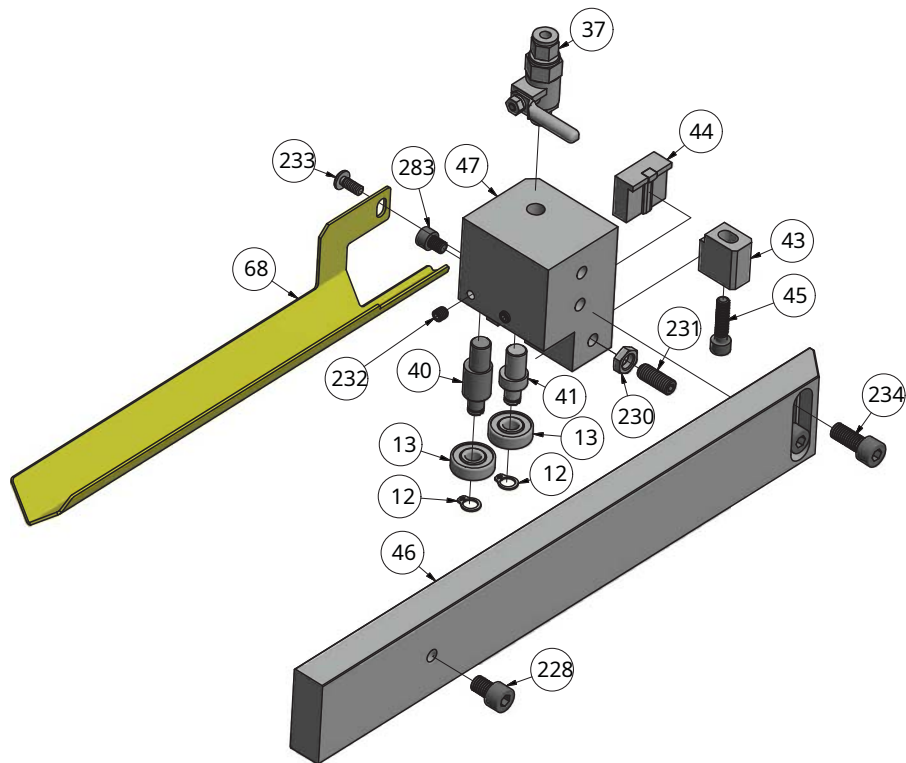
Explosionszeichnung - Dibujo de piezas de repuesto
